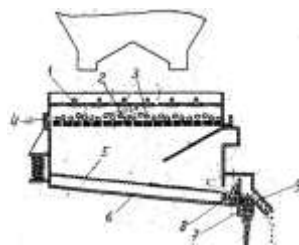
Установка выбивки форм и дробления комьев отработанной смеси [33]
